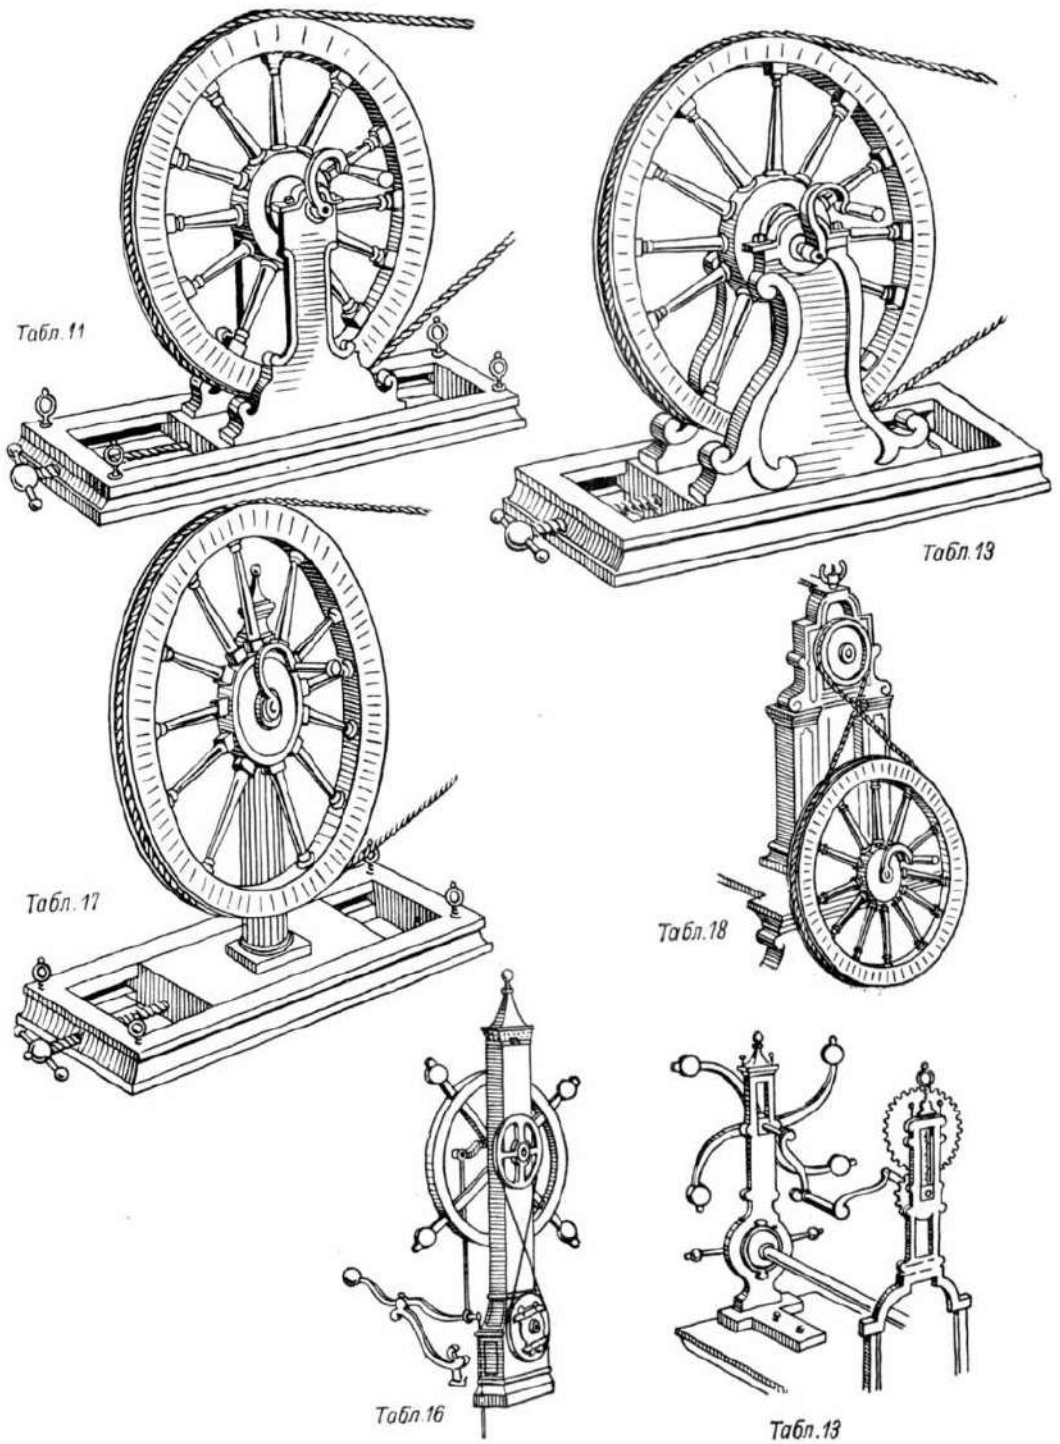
Конструкции маховых колес и натяжных устройств для привода
